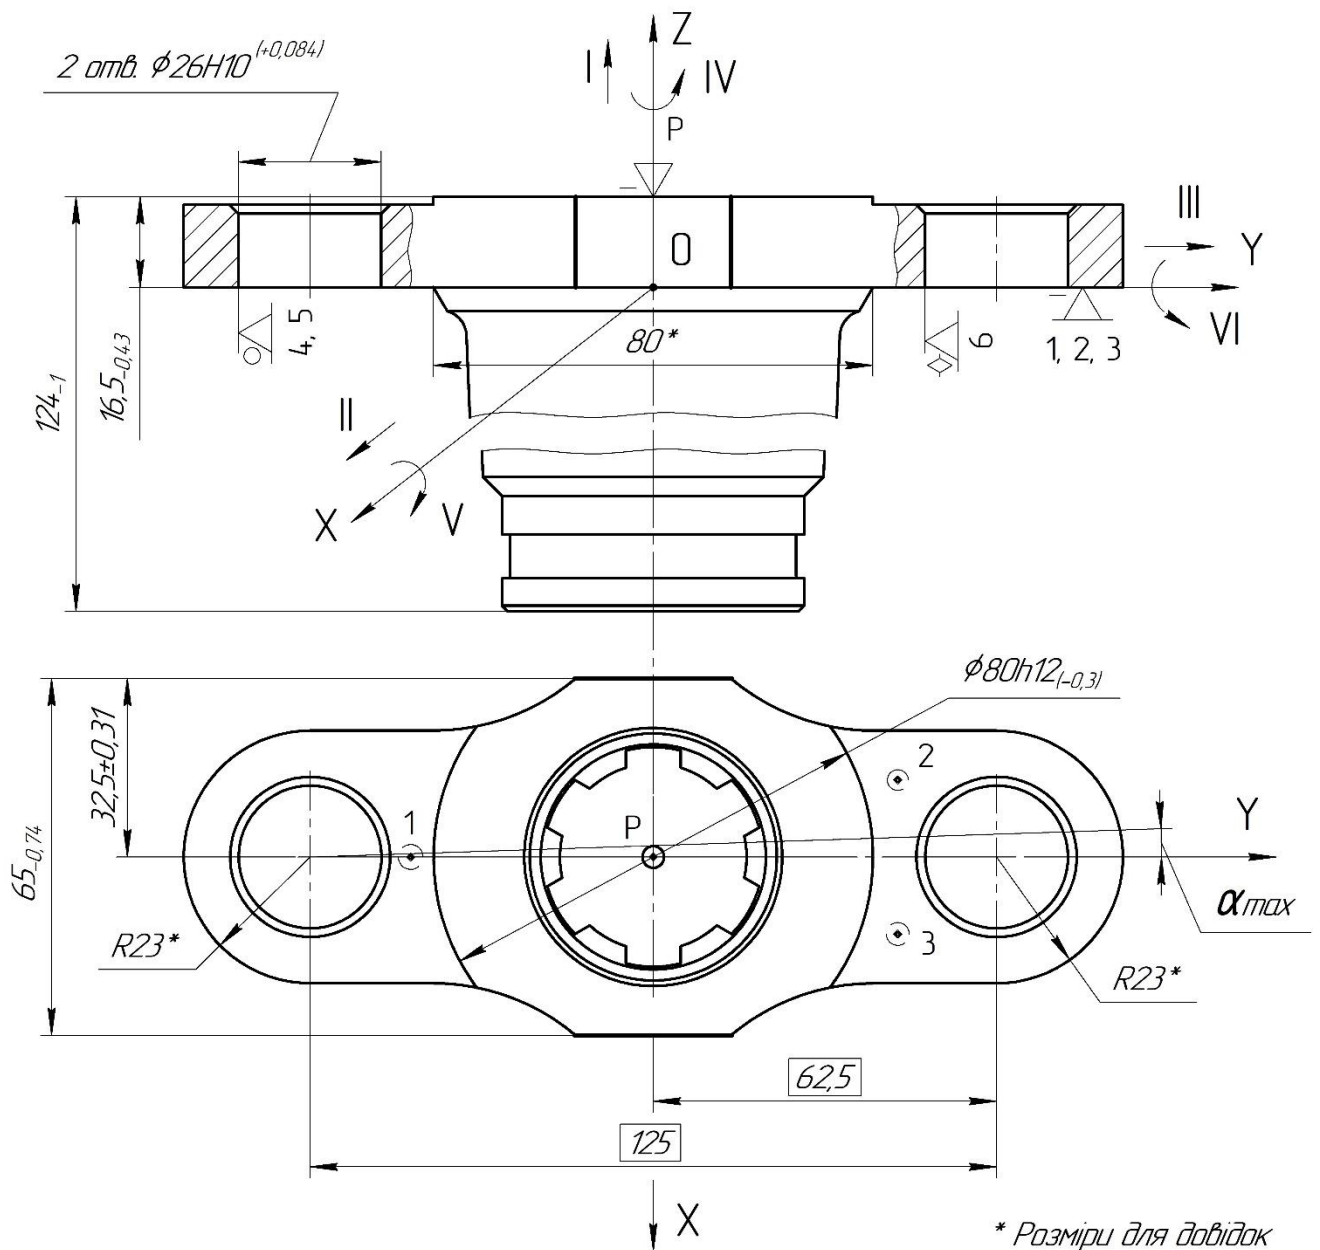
Ескіз заготовки на операції 040 «Горизонтально-фрезерна»
